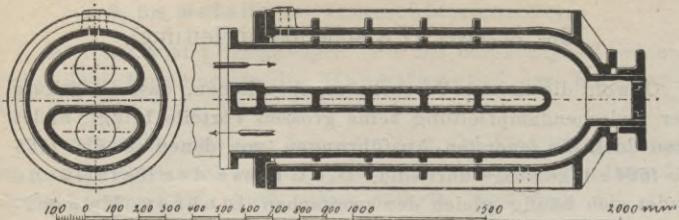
Receiver I zur Dreifach-Expansionsmaschine.
